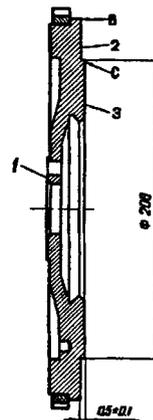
Маховик: 1 - поверхность крепления к фланцу коленчатого вала; 2 - поверхность крепления сцепления; 3 - опорная поверхность ведомого диска сцепления; В - место проверки биения поверхности 2; С - место проверки биения поверхности 3
